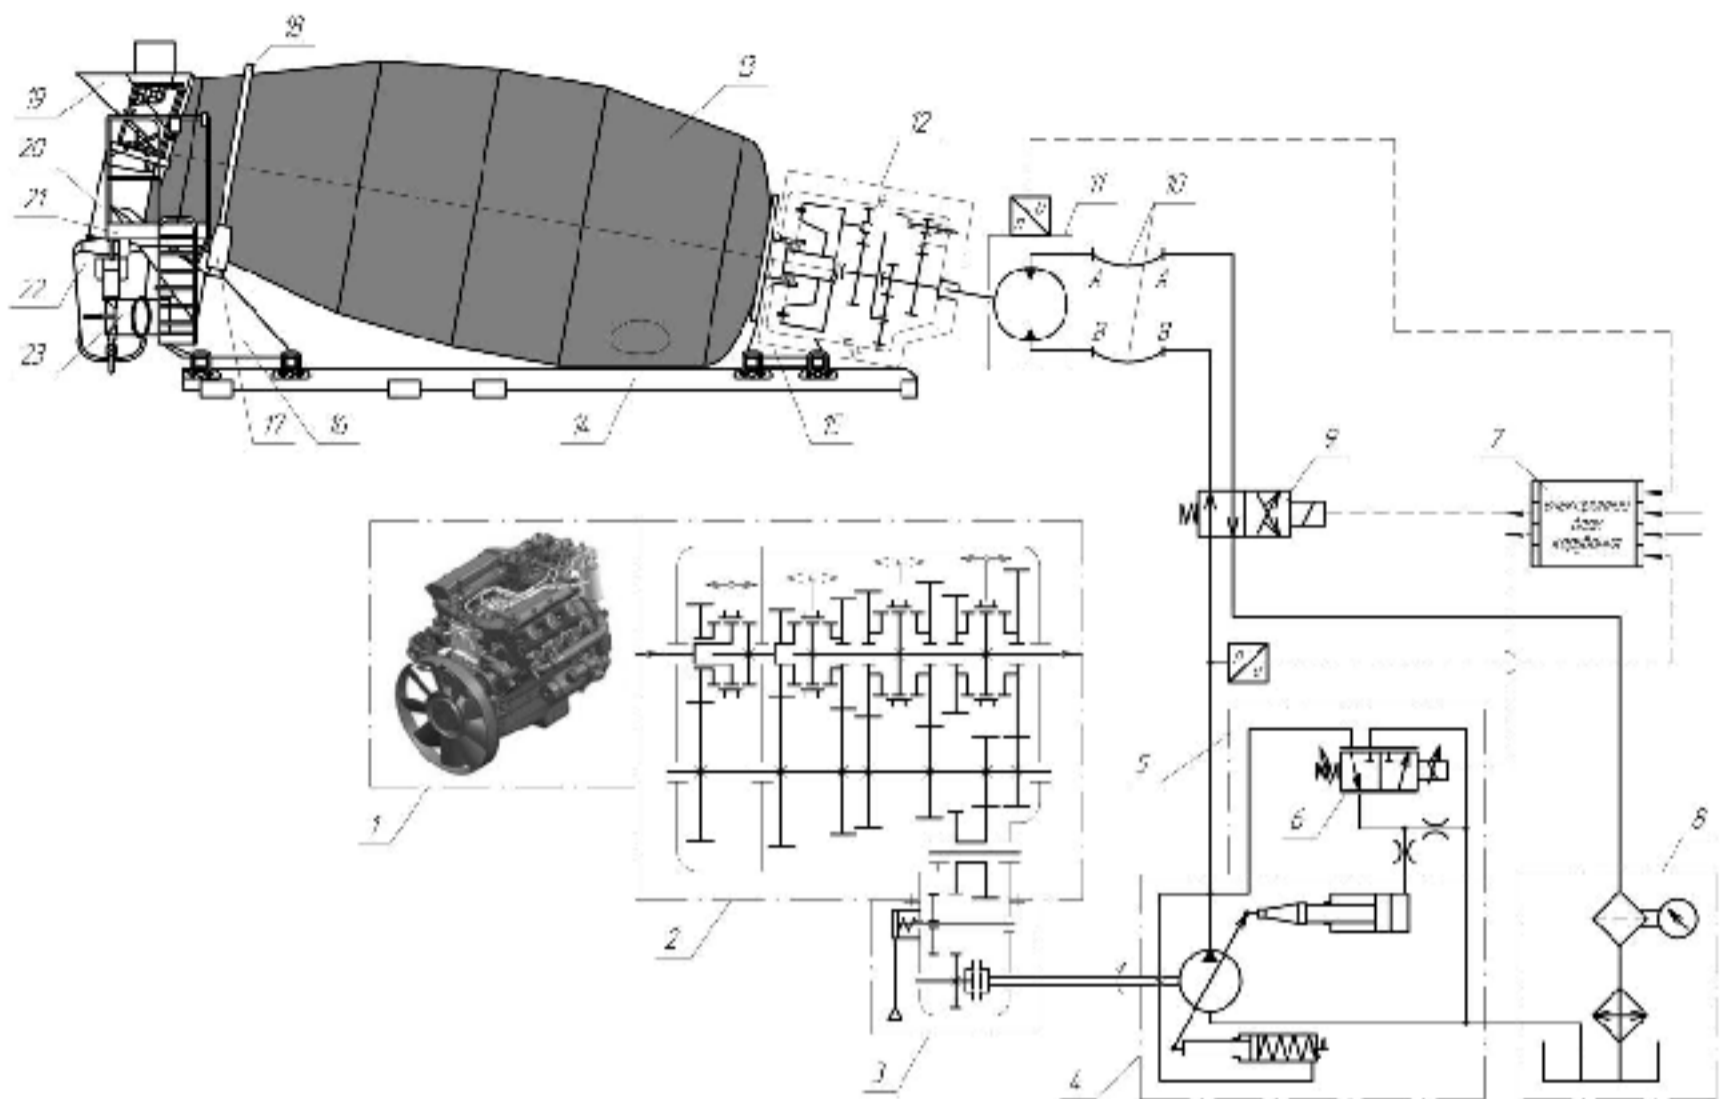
Принципова схема гідромеханічного приводу обертання змішувального барабана АБЗ:
